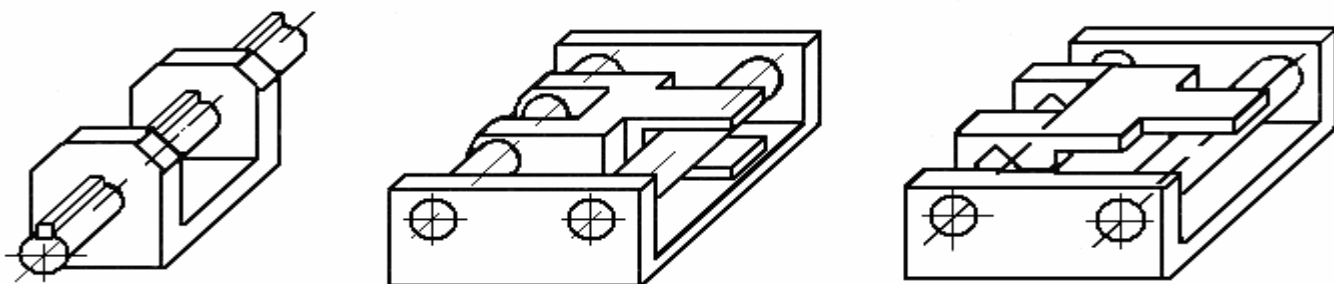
Цилиндрические направляющие с устройством для предотвращения проворачивания
